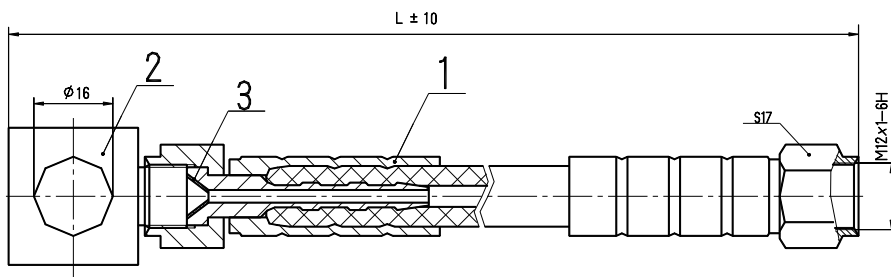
Габаритные и присоединительные размеры шланга ШГ - 15:
